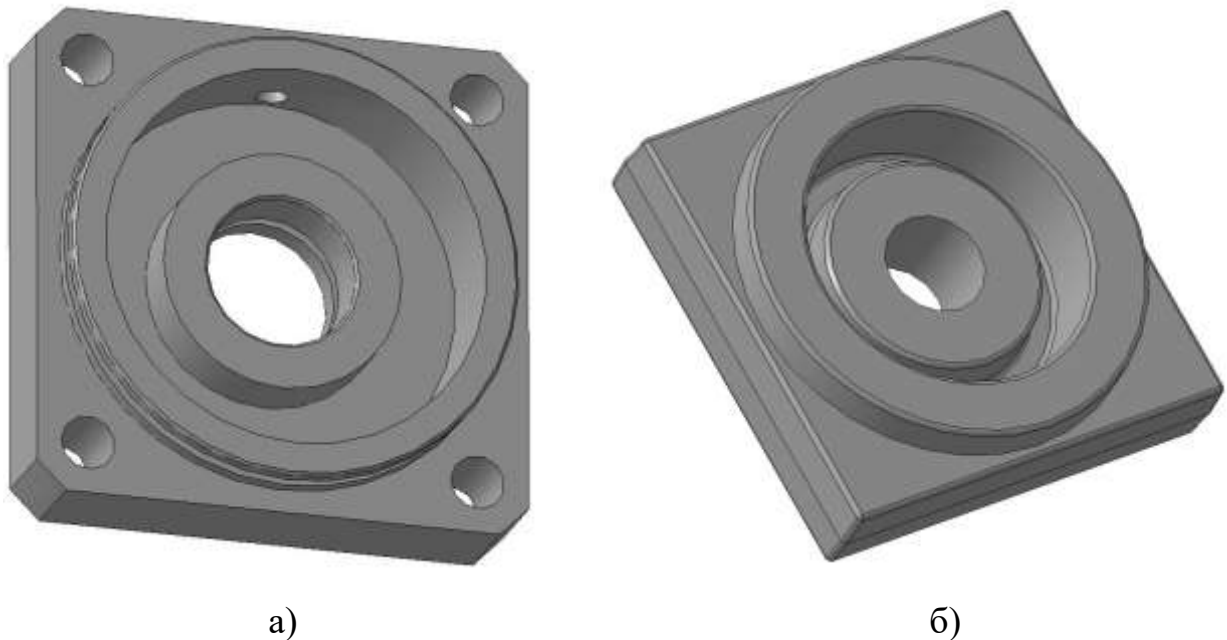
Моделі деталі а) та заготовки б)
